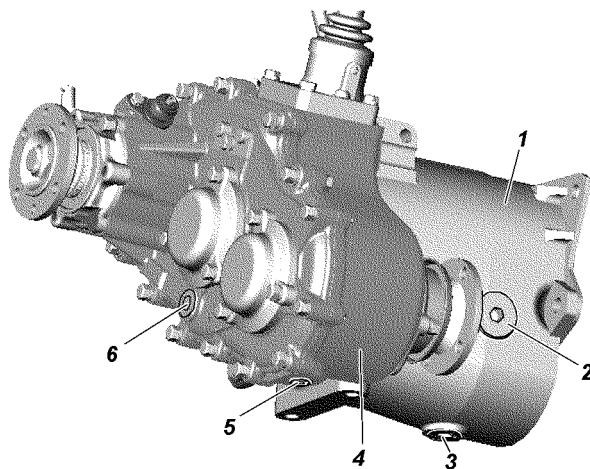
Четырехступенчатая коробка передач и раздаточная коробка: 1 -коробка передач; 2 -пробка заливного отверстия картера коробки передач; 3 -пробка сливного отверстия картера коробки передач; 4 -раздаточная коробка; 5 -пробка сливного отверстия картера раздаточной коробки; 6 -пробка заливного отверстия картера раздаточной коробки
